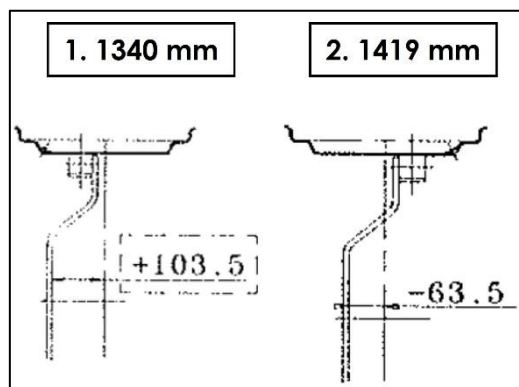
RÉGLAGE DE LA VOIE ARRIÈRE
